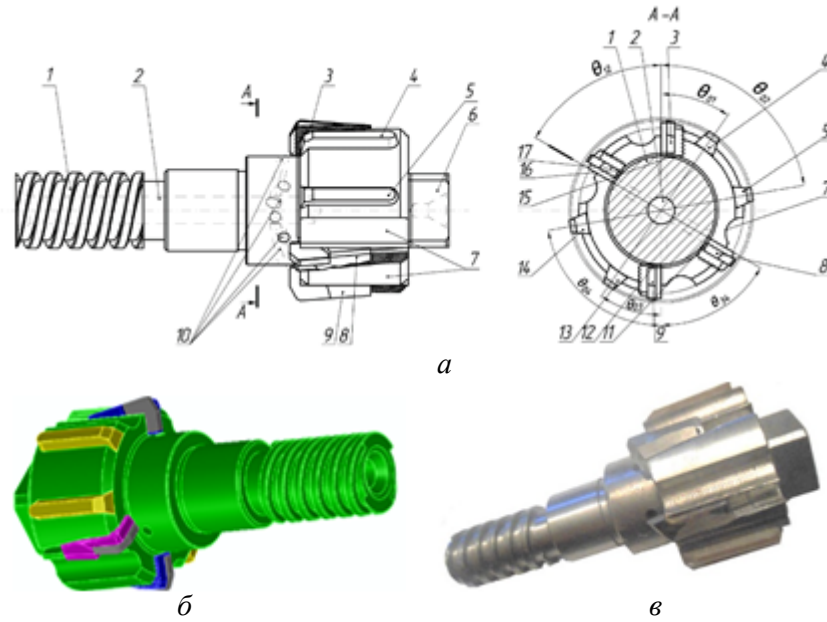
Конструкція розточувального інструменту з парно-асиметричним розміщенням лез: а – конструктивна схема; б – 3-D модель; в – фотографія
